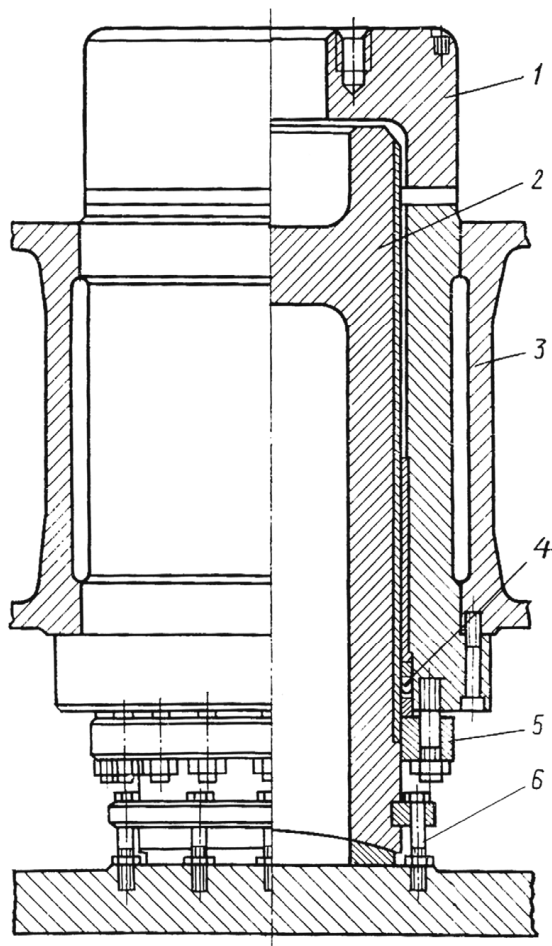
Цилиндр гидравлического пресса плунжерного типа:
